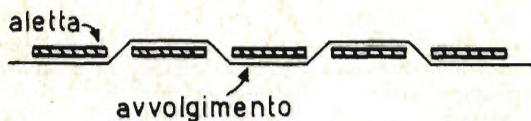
Il disegno illustra il percorso del filo lungo le diverse alette.
